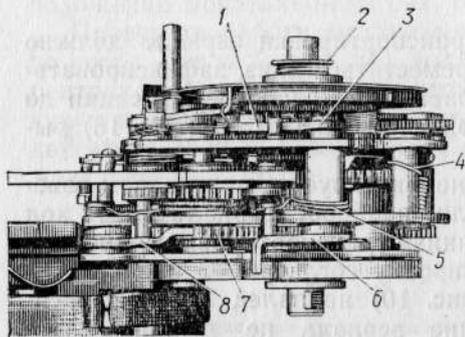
Механизм транспортировки на корпусе зеркала (вид сбоку):
